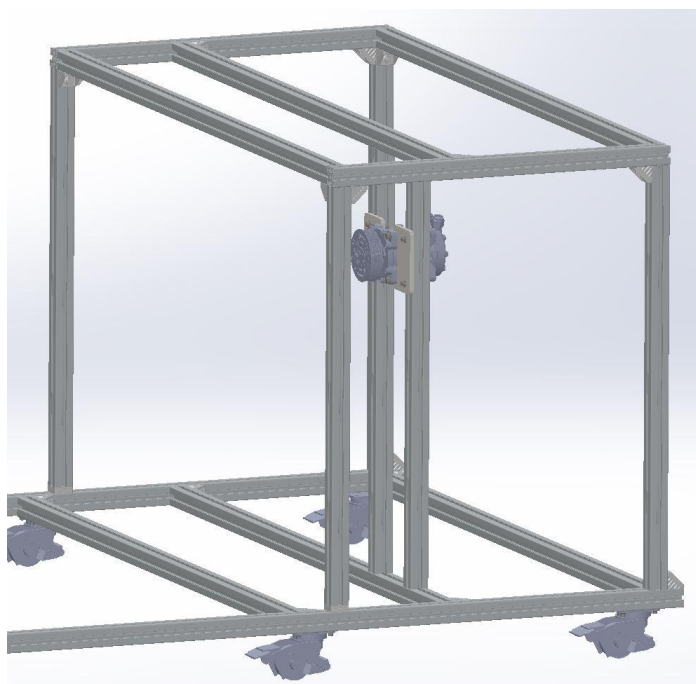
Rám elektromotoru s motorem a pojezdovými koly
